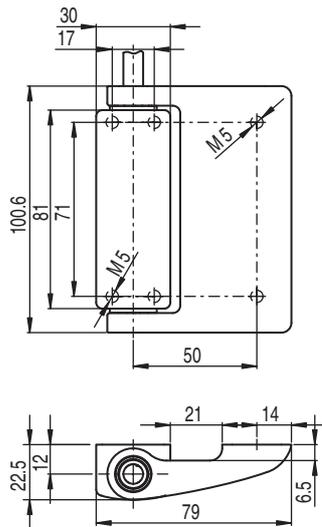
Dimensioni dell'S410-M1CB2-T in mm
